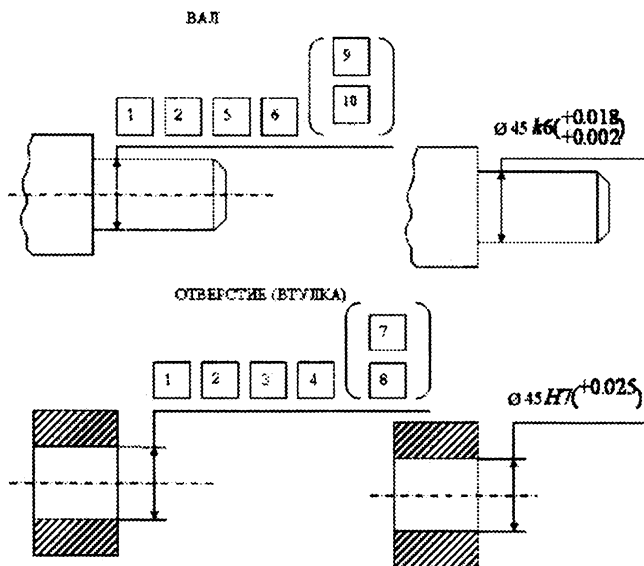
Обозначение допусков на чертежах деталей (номера зон соответствуют рис. 4.8)
